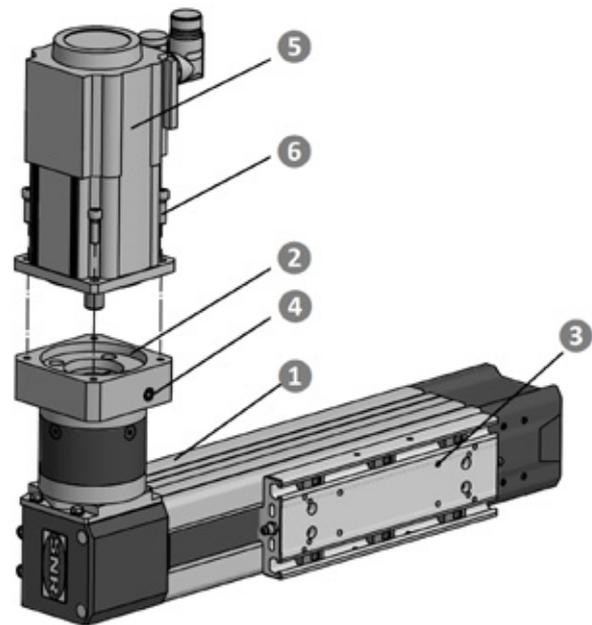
Entraînement sur module linéaire avec réducteurs planétaires
